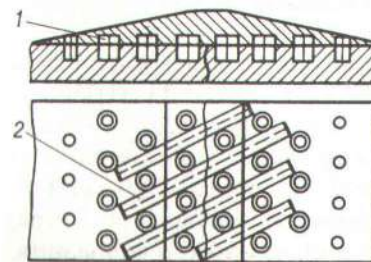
Схема розташування сталевих зв'язок у металі шва при холодному зварюванні чавунів:
